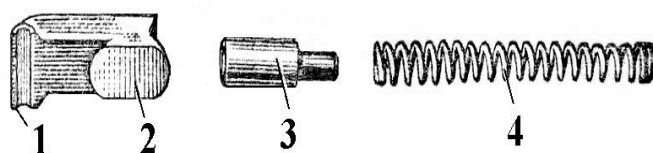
Выбрасыватель (1 — зацеп; 2 — пяточка для соединения с затвором;
